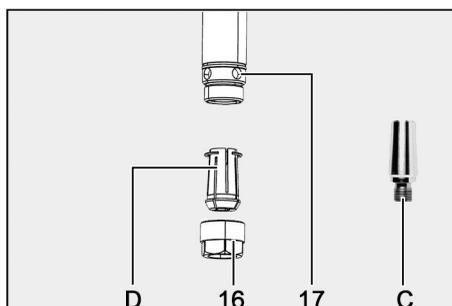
Pinza, tuerca de racor, adaptador y husillo de fresado
